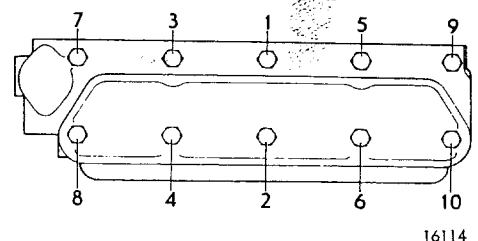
Dragningsföljd för cylinderlockets skruvar
